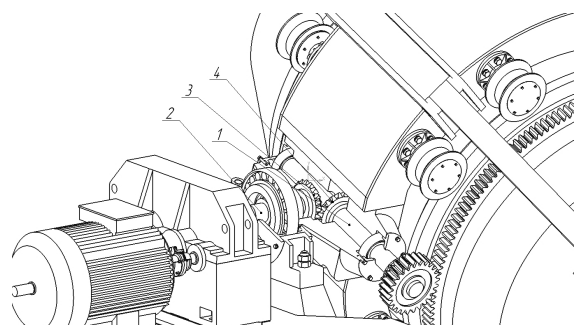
Предложенная конструкция механизма вращения корпуса кислородного конвертера
